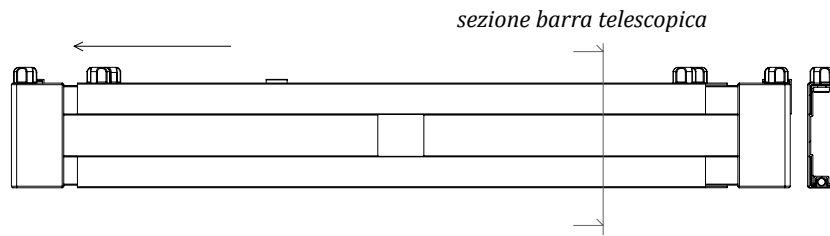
Barra telescopica: dettaglio scorrimento
